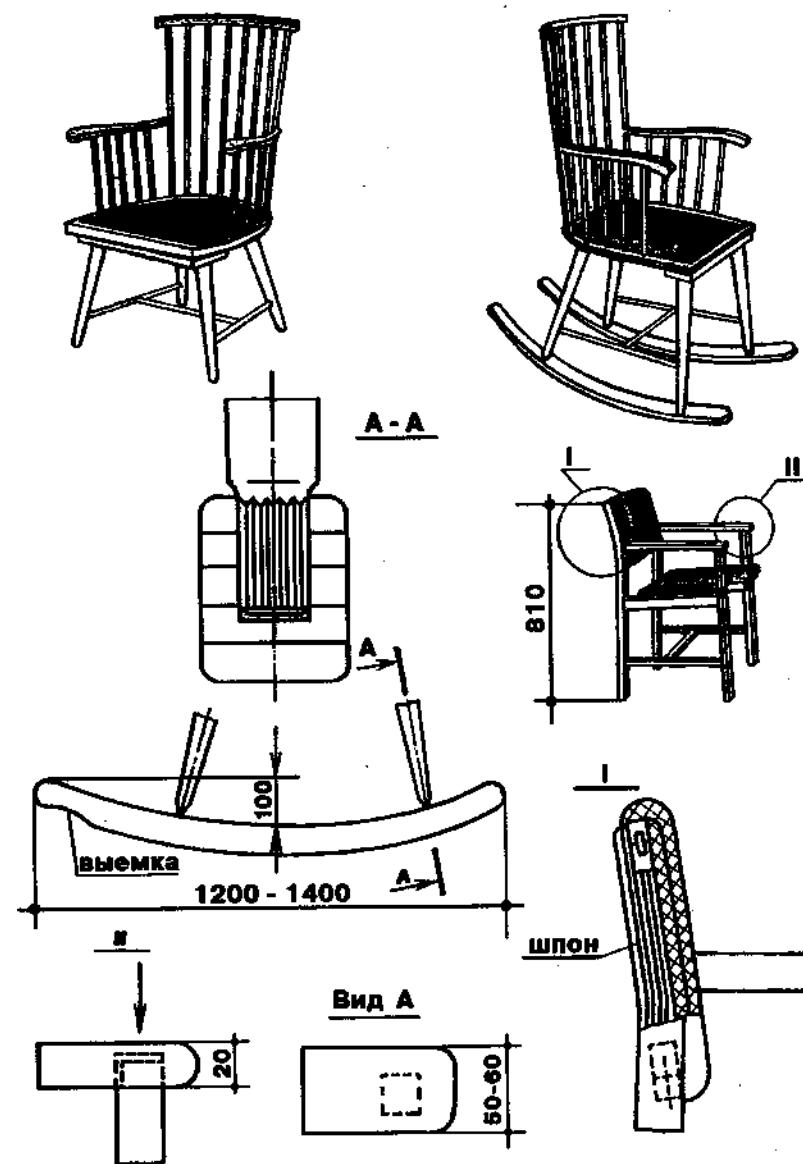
Конструкция рабочих кресел и кресла-качалки
